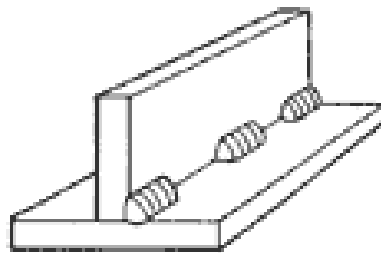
Soldagem intercalada (AWS, 2001).
